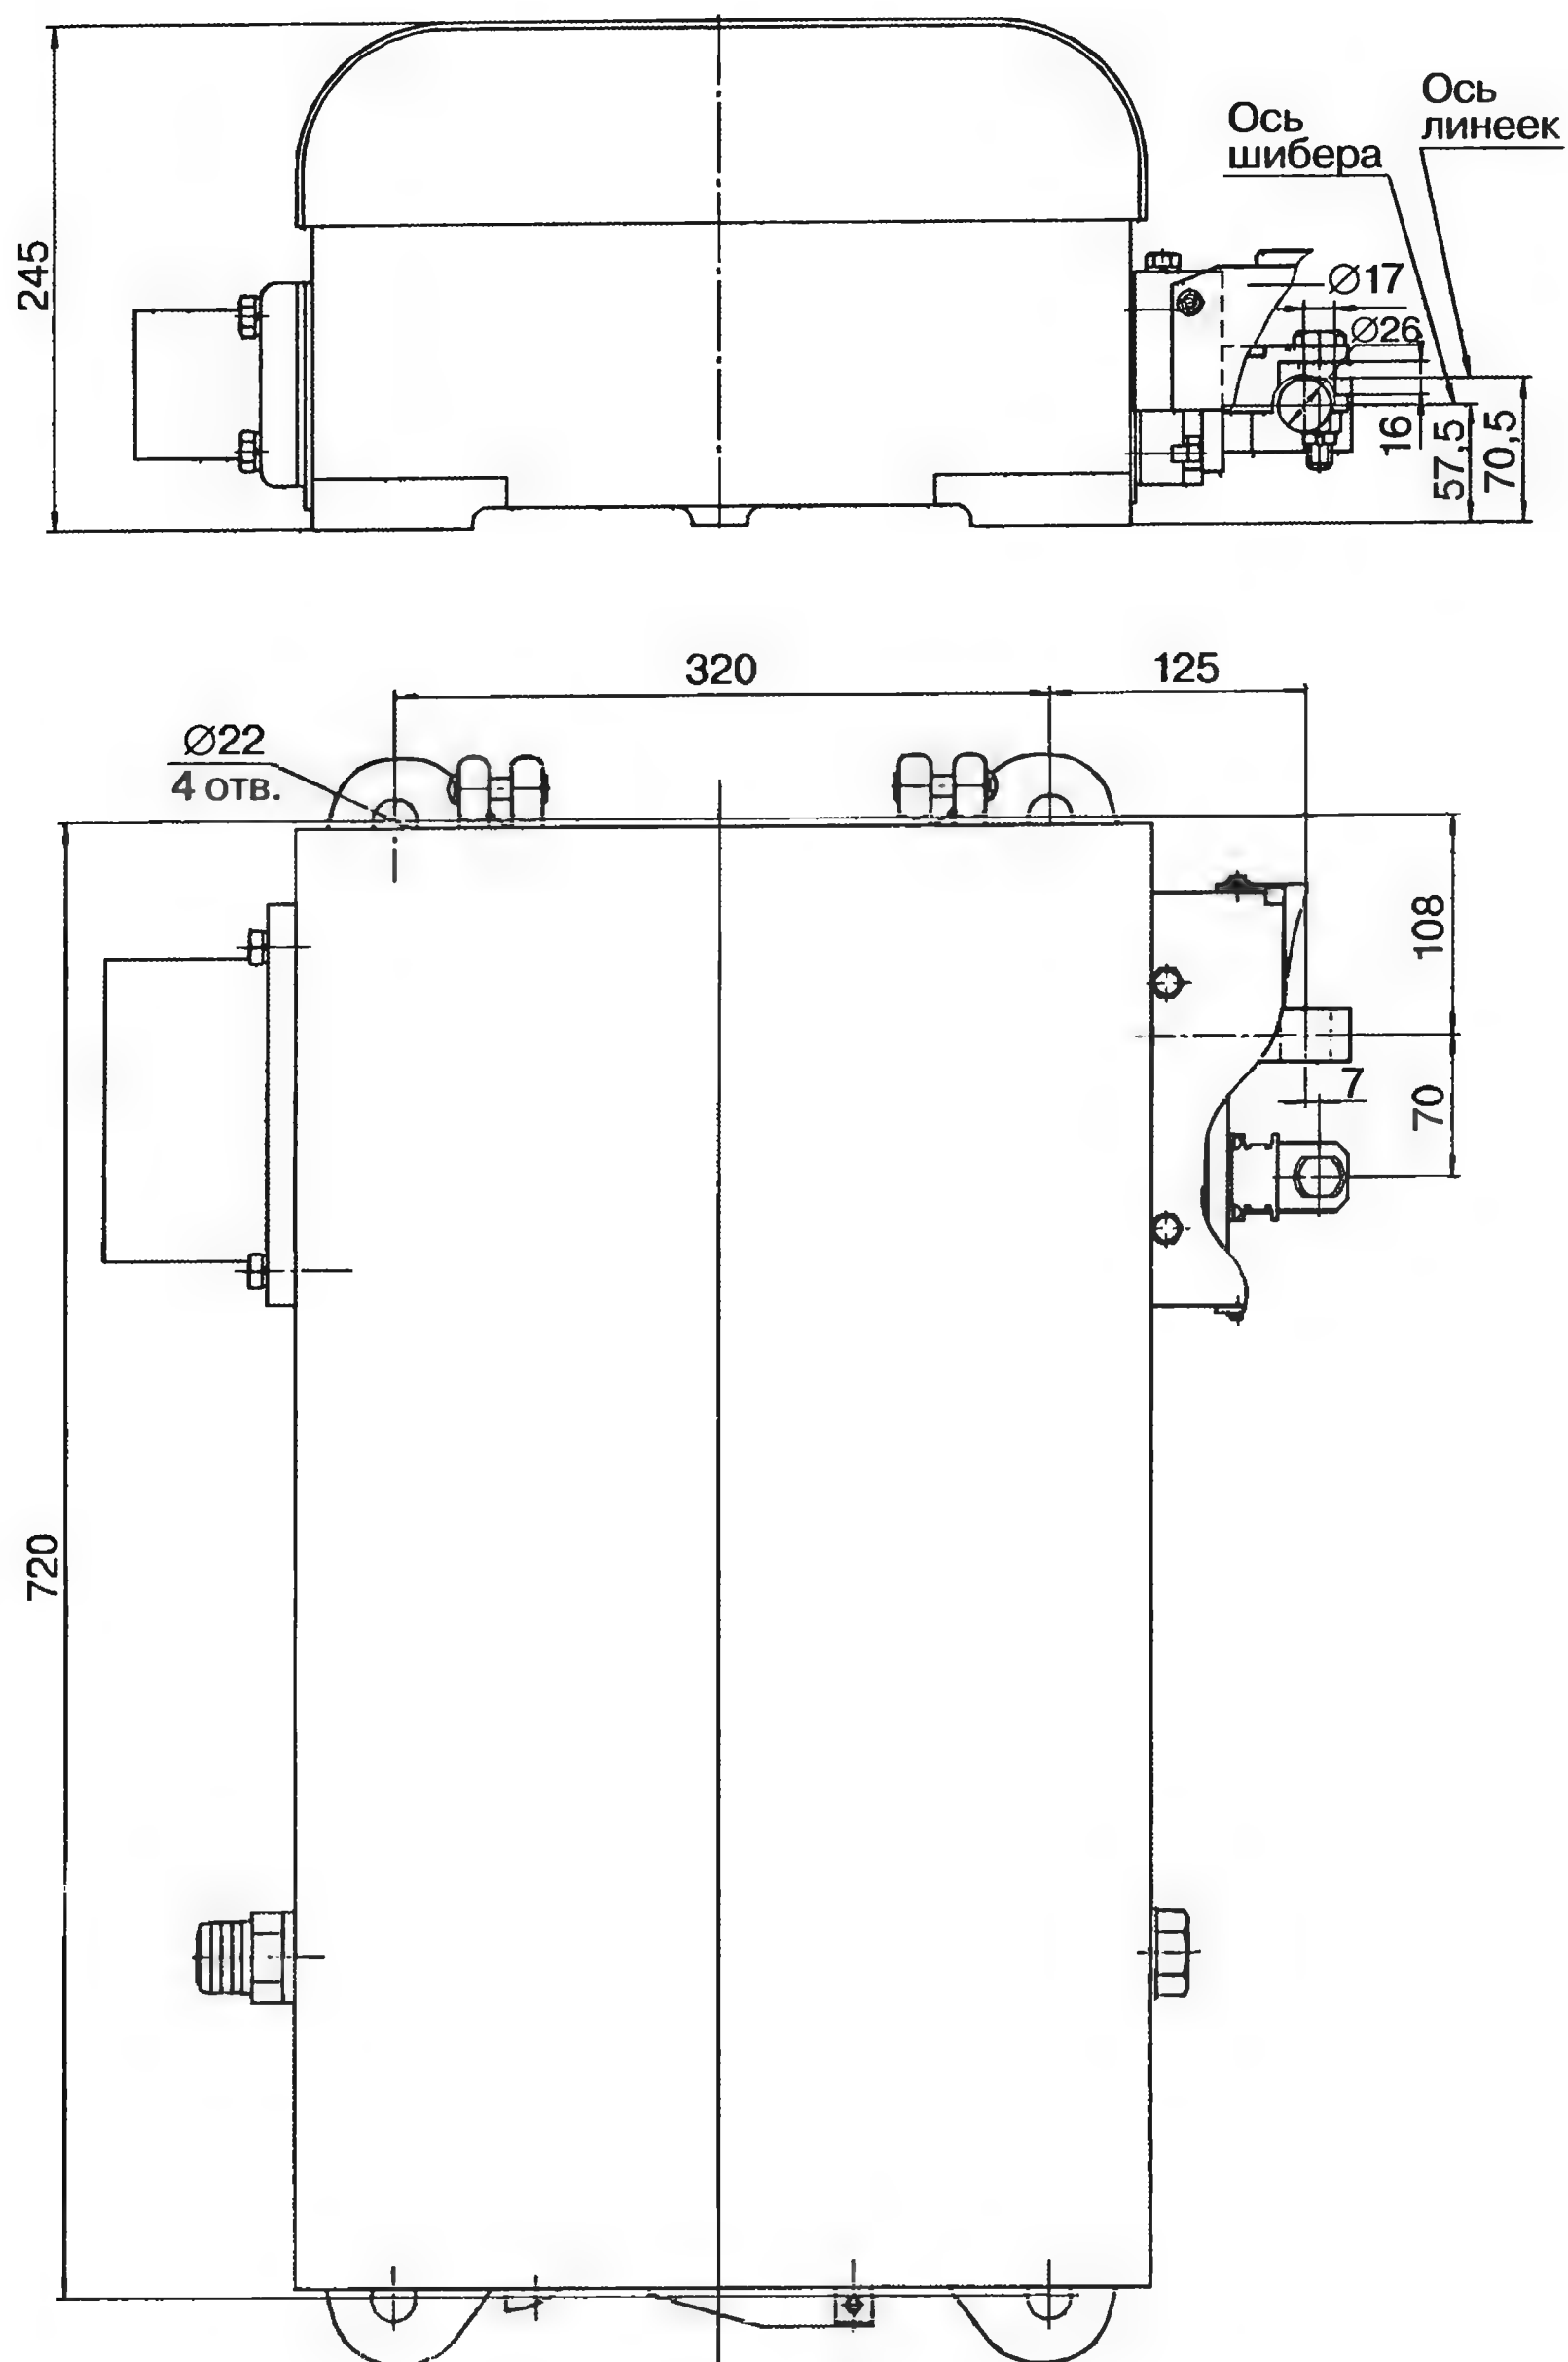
Электропривод стрелочный СП-12К. Установочные и присоединительные размеры
